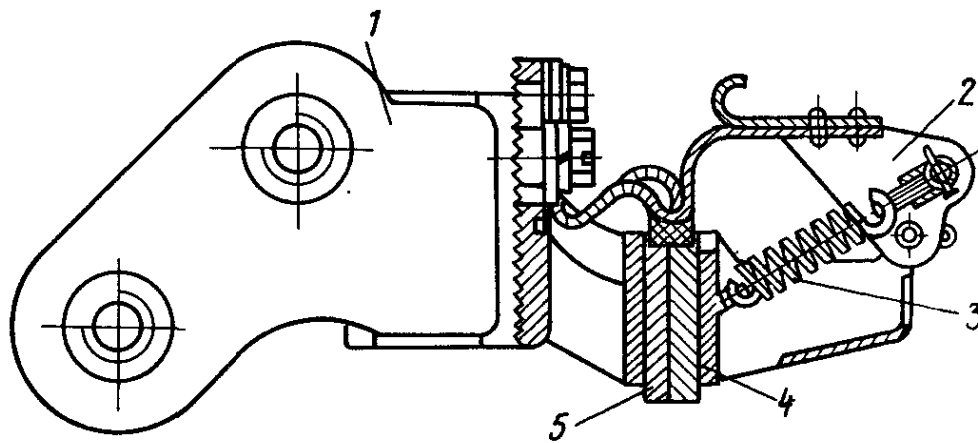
Щеткодержатель с пластмассовым кронштейном тягового двигателя НБ-406Б:
